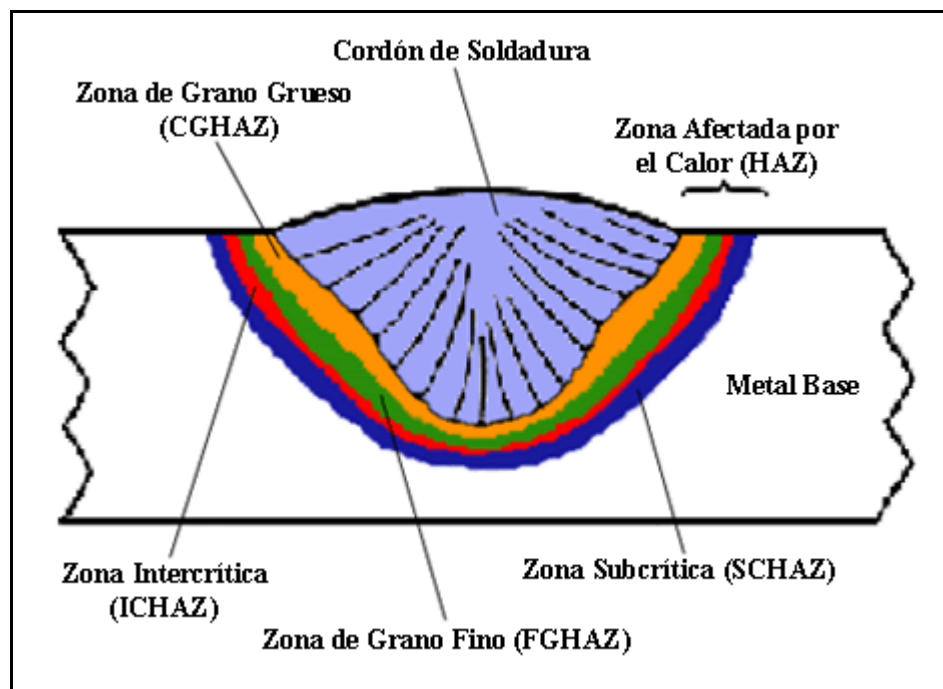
Regiones de un pase simple de soldadura.
